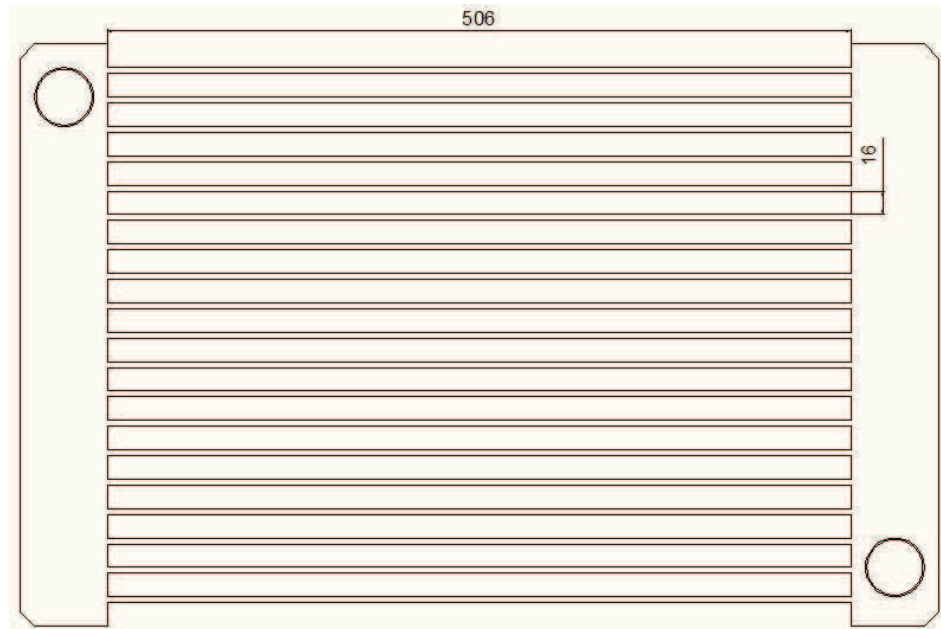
Geometría del radiador sin aletas. Altura del radiador = 374mm
